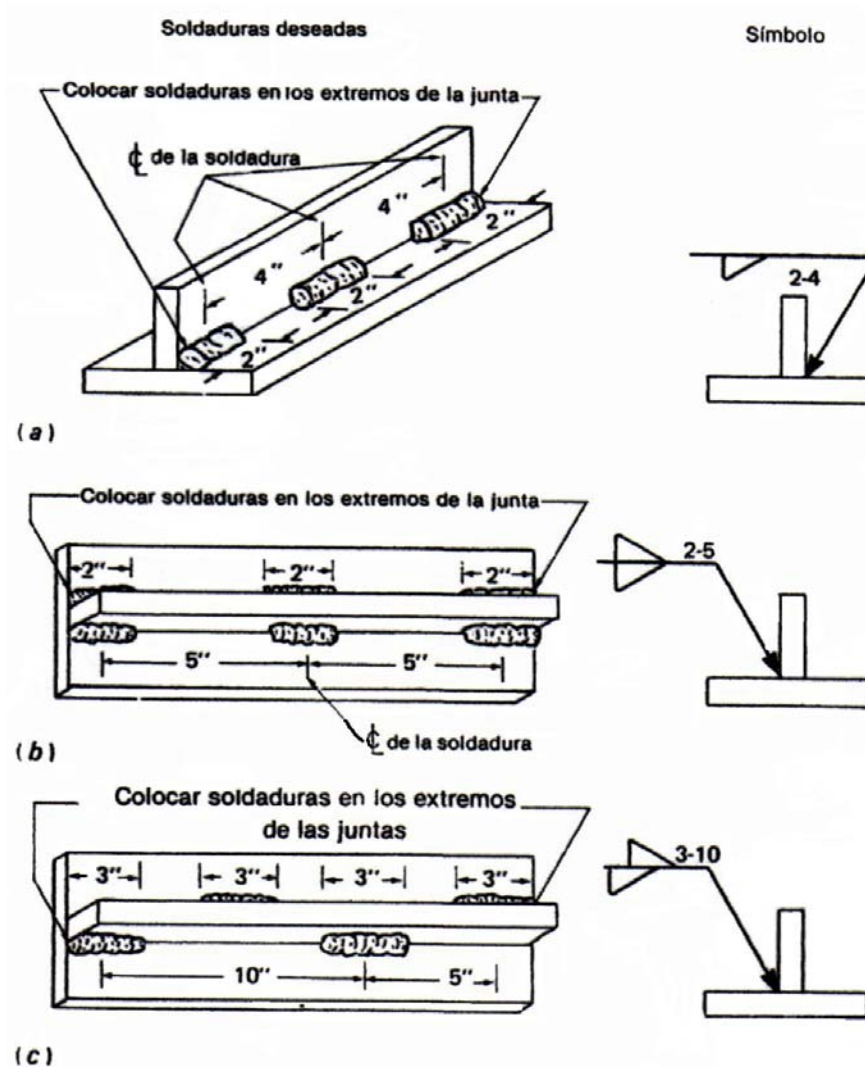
Símbolos de soldadura en los que se especifican la longitud y el paso de las soldaduras: a) soldadura intermitente; (b) soldadura intermitente de cadena; (c) soldadura intermitente escalonada.
